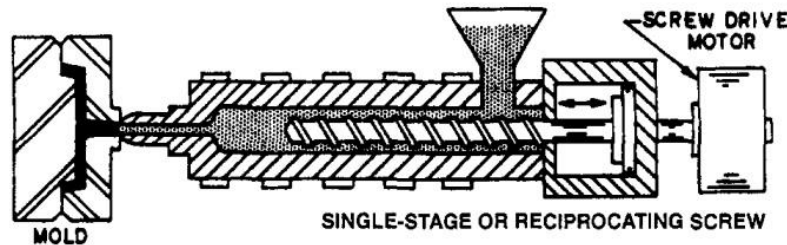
Máquina de tornillo recíproco. (Fuente [11])
